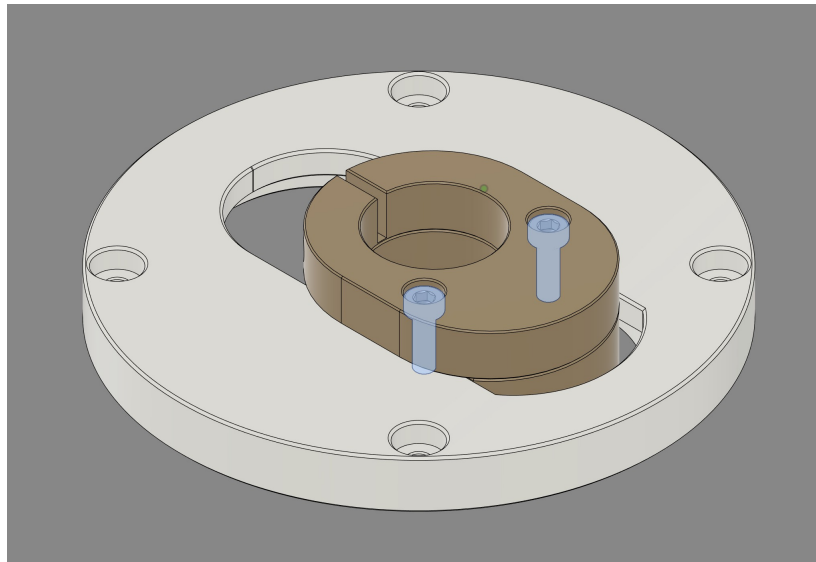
Plattenspieler-Basis (hier für einen PTP 12)
